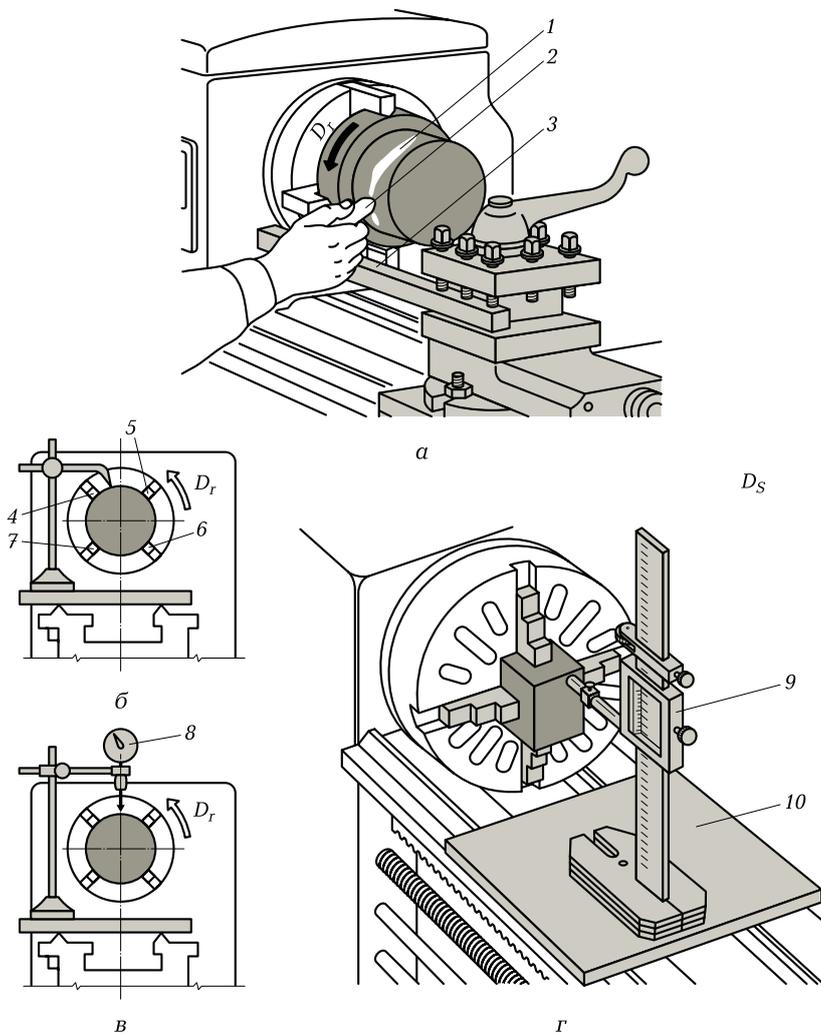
Выверка заготовок, закрепленных в четырехкулачковом патроне: а — выверка «на мелок»; б — выверка по рейсмасу; в — выверка по индикатору часового типа; г — выверка по штангенрейсмасу; 1 — заготовка; 2 — мелок; 3 — упорная планка; 4—7 — кулачки патрона; 8 — индикатор часового типа; 9 — штангенрейсмас; 10 — плита; D_r — главное движение
